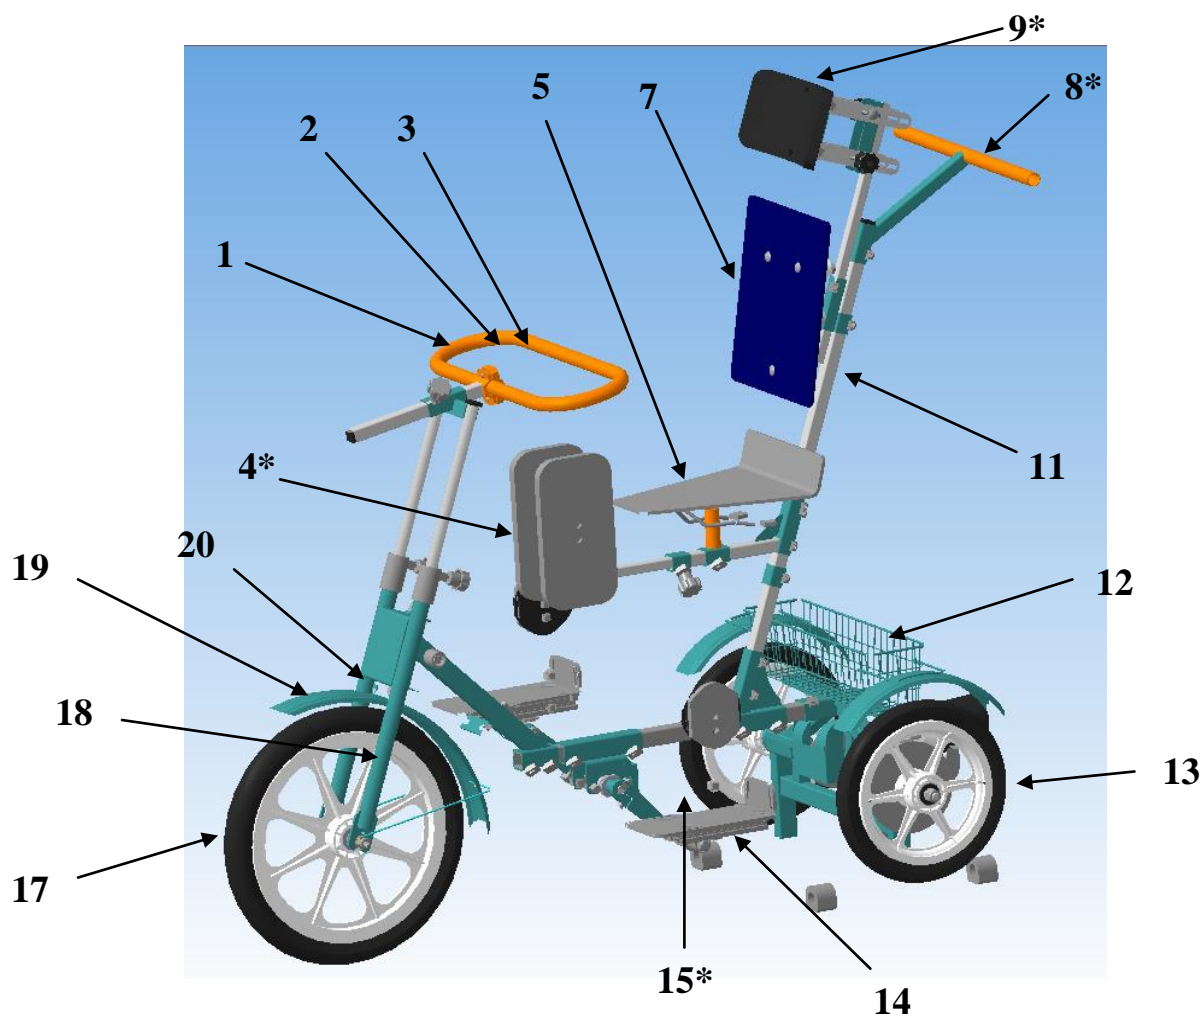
Внешний вид велоколяски и схема расположения деталей и узлов
